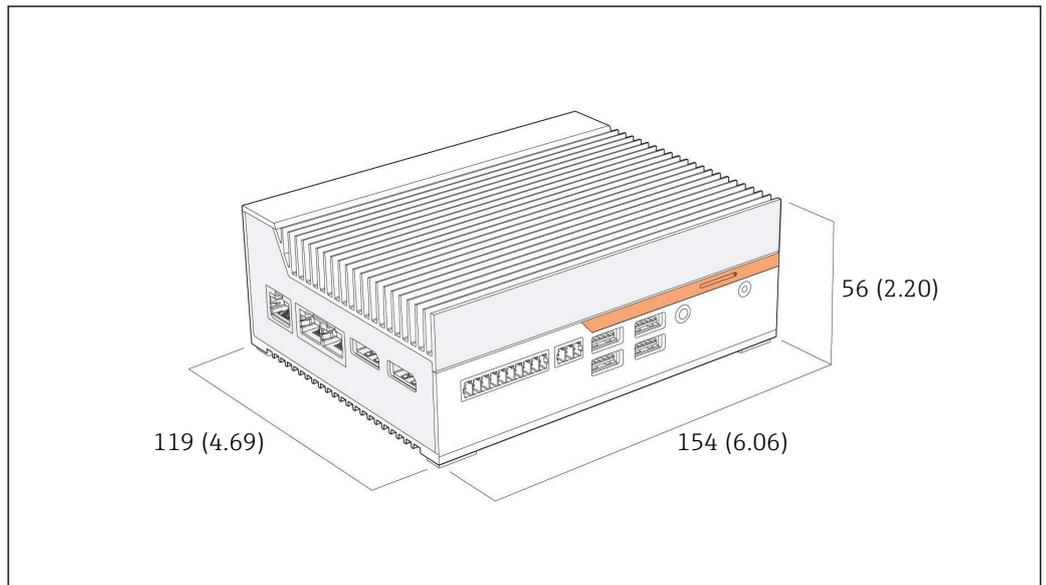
SGC500 的外形尺寸示意图; 单位: mm (in)
